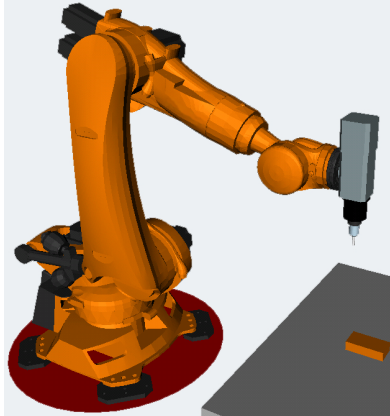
6-achsiger Knickarmroboter mit Frässpindel
